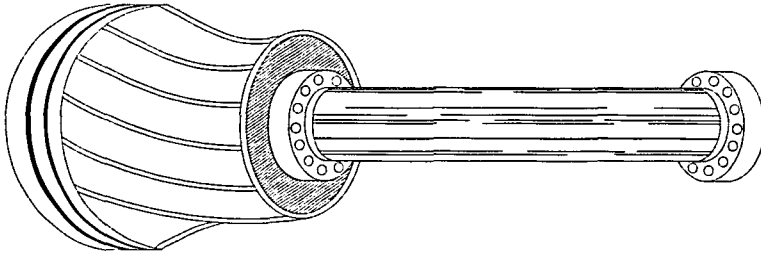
Rotor de turbina Francis. P = 68 000 KW, N = 280.8 rpm, H = 110 m. Instalado en Cambambe, Angola. (Escher Wyss).
